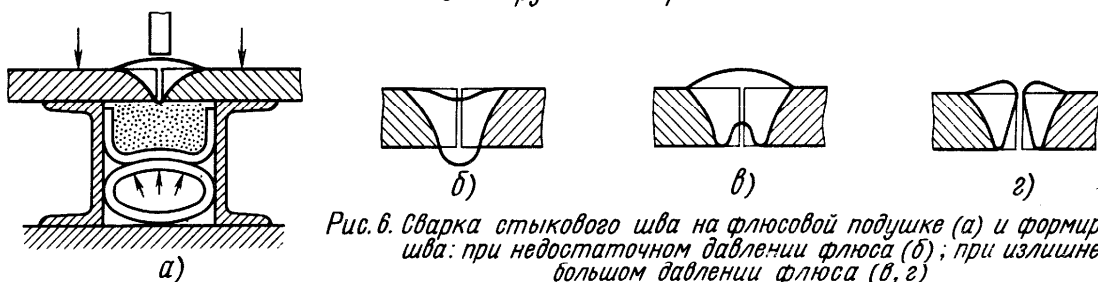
Сварка стыкового шва на флюсовой подушке (а) и формирование шва: при недостаточном давлении флюса (б); при излишке большом давлении флюса (в, г)
